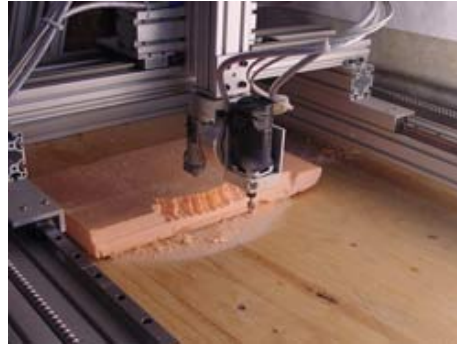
Trabajos de manufactura en plástico con Routers CNC.
